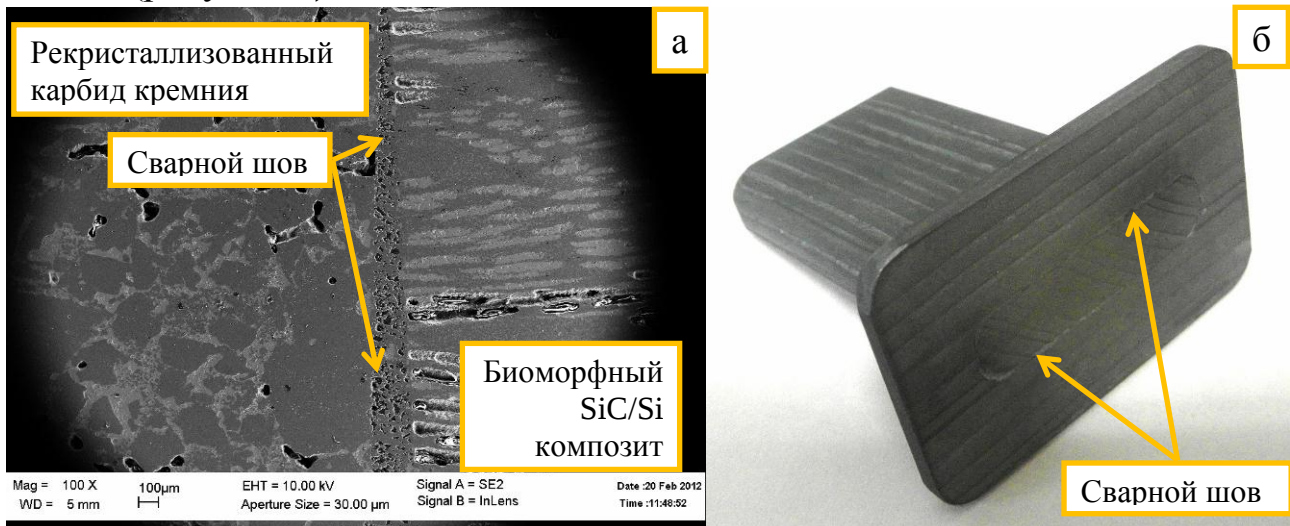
Сварка карбидокремниевых материалов: а – микроструктура сварного шва между рекристаллизованным и биоморфным карбидом кремния; б – изделие сложной формы полученное сваркой деталей из биоморфного SiC/Si композита.
